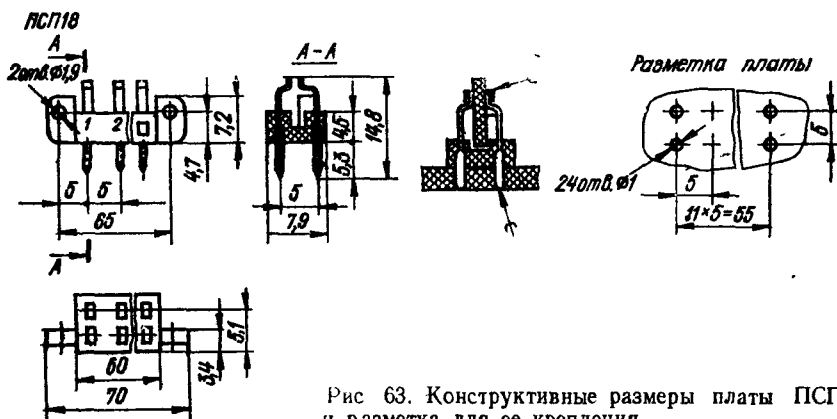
Конструктивные размеры платы ПСП18 и разметка для ее крепления
